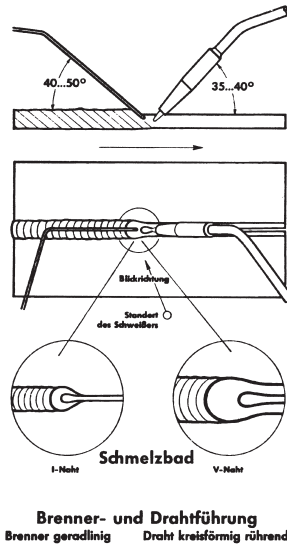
Nachlinks- und Nachrechtsschweissen
